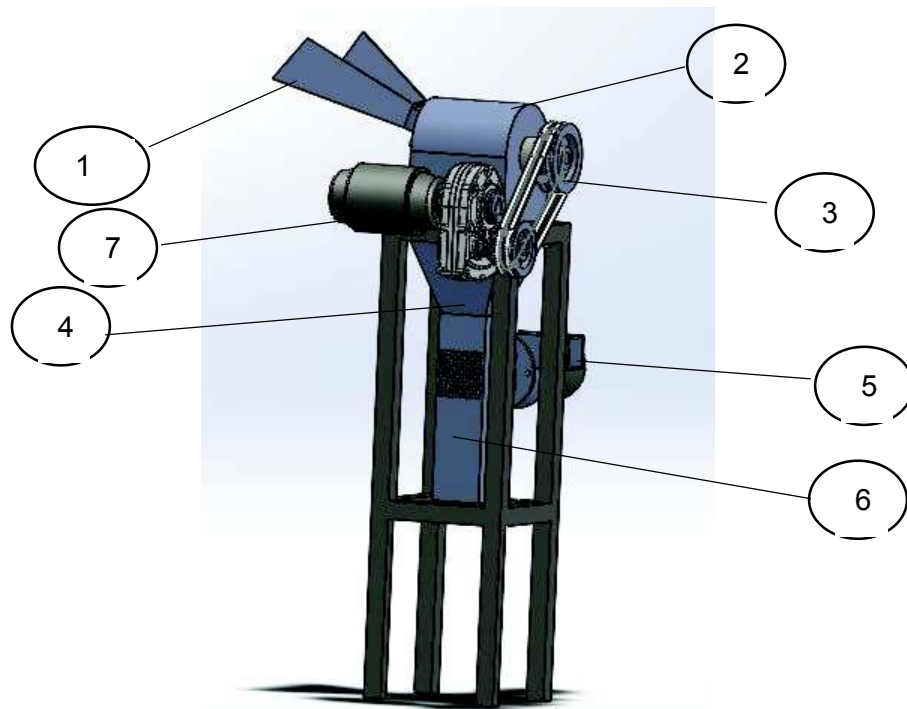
Bosquejo de la máquina desecapsuladora y descascaradora de sachá inchi.
